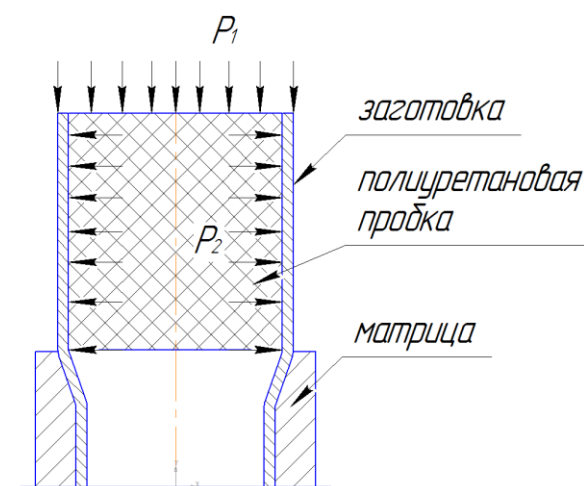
Схема процесса комбинированного редуцирования-раздачи трубчатой заготовки
